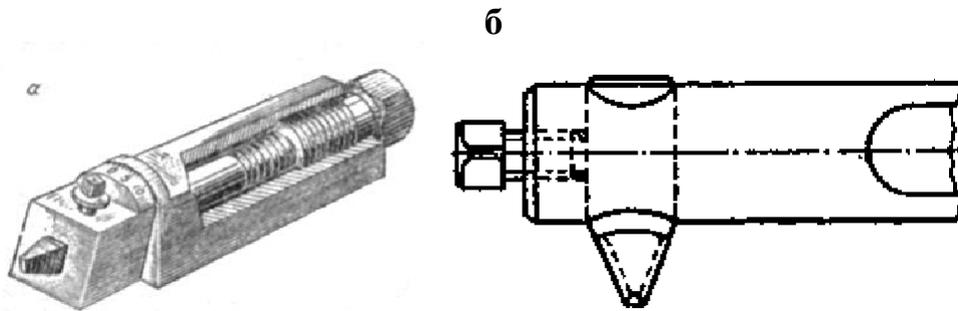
Державки для поворота резьбовых резцов на угол подъёма
